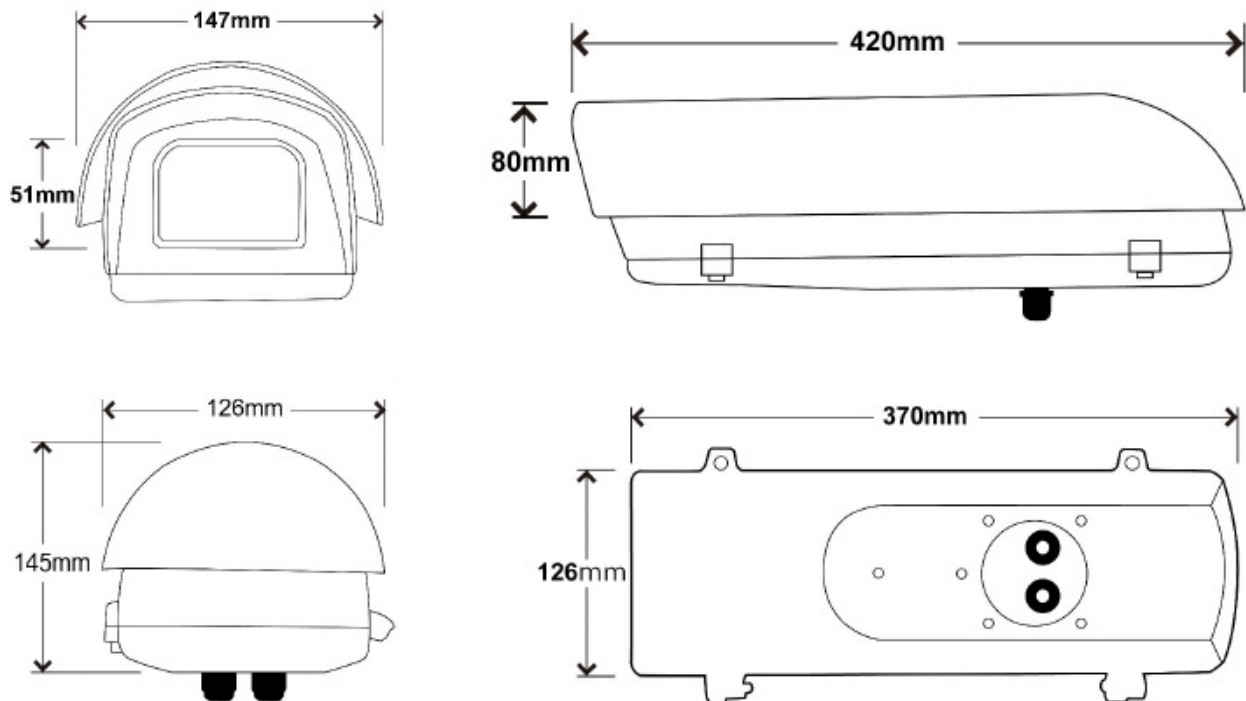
Габаритный чертеж видеокамеры ИВМ-602.
